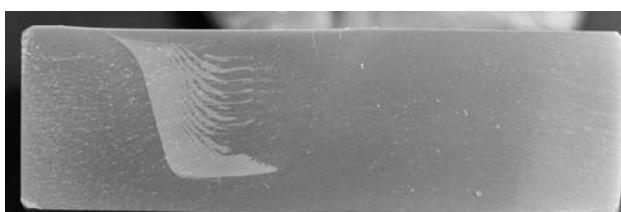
Макрошлиф образца сплава 6082 после сварки на воздухе
